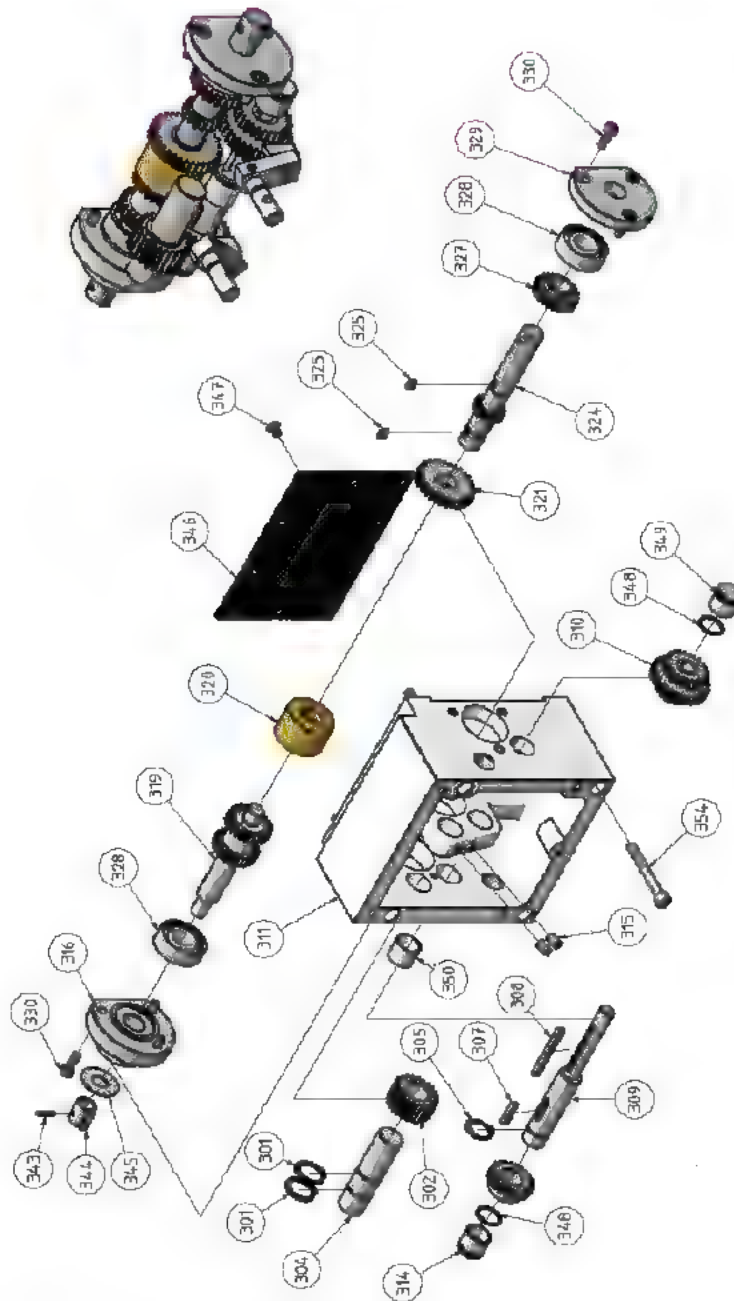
Vorschubgetriebe D240 2 von 2 - Feed gear D240 2 of 2
